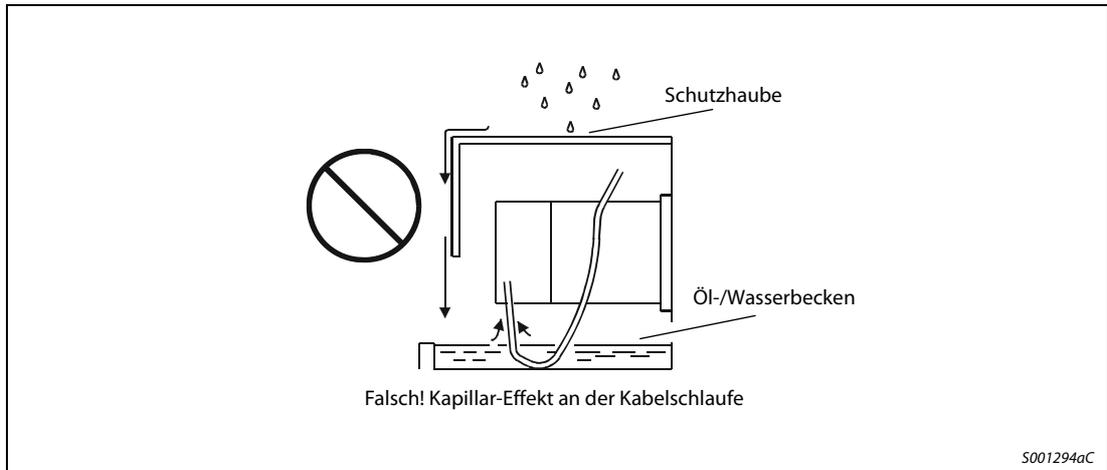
Kabel zum Motor nicht in Öl oder Wasser liegend verlegen
